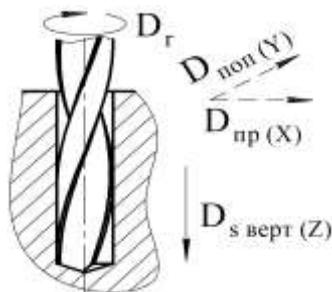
Формообразующие движения вертикально-сверлильного станка
